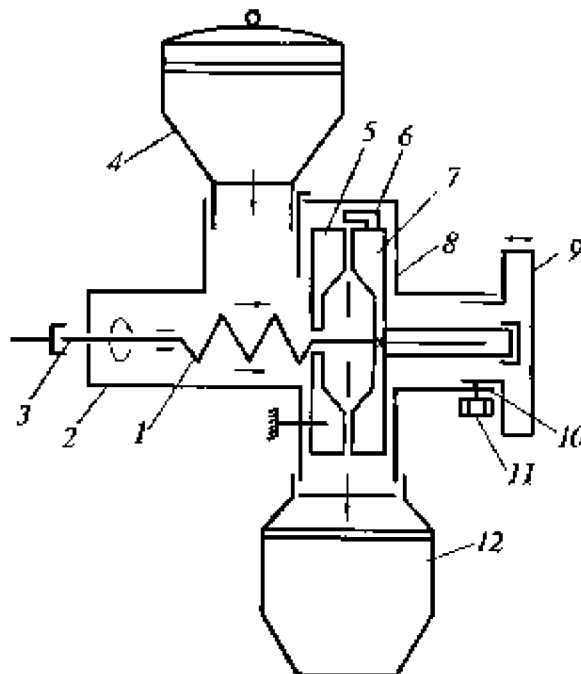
Механізм для розмелювання кави ММК-120: 1 – шнек; 2 – корпус; 3 – вал робочий; 4 – бункер завантажувальний; 5 – жорно нерухоме; 6 – лопатка; 7 – жорно, що обертається; 8 – кришка; 9 – гайка; 10 – хвостовик; 11 – гвинт; 12 – бункер приймальний
